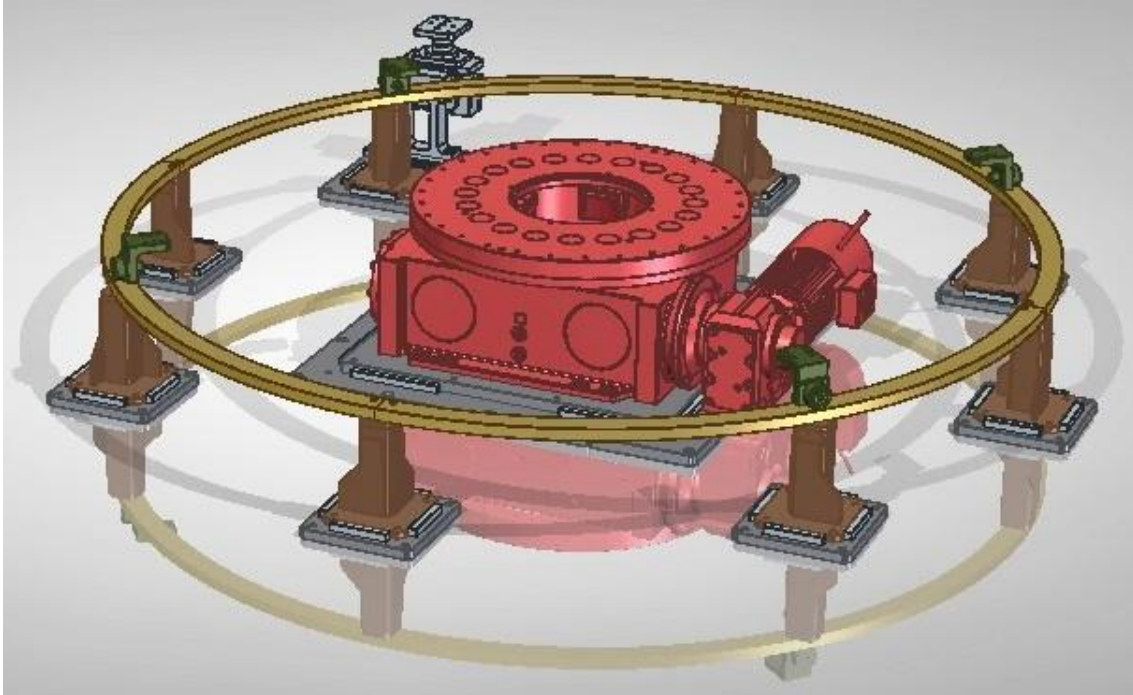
Diseño del conjunto “Estructura de montaje”
